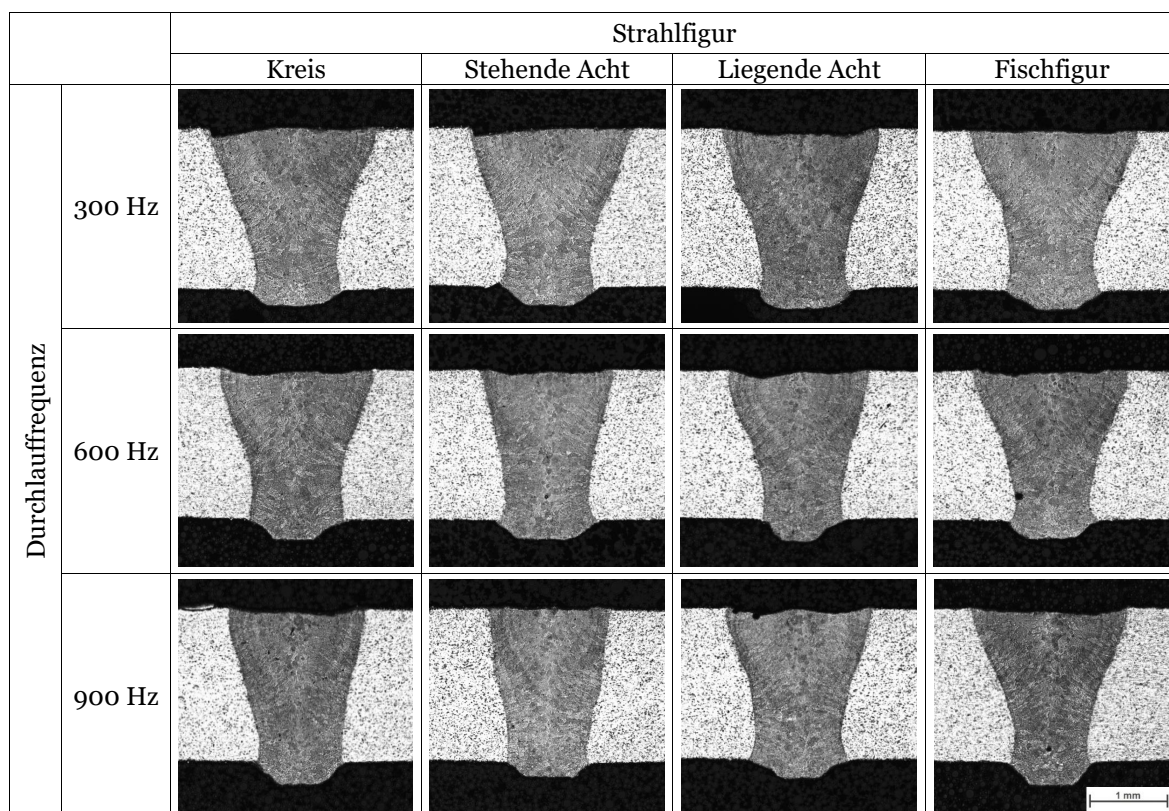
Sichtbare Schweißnahtfehler
